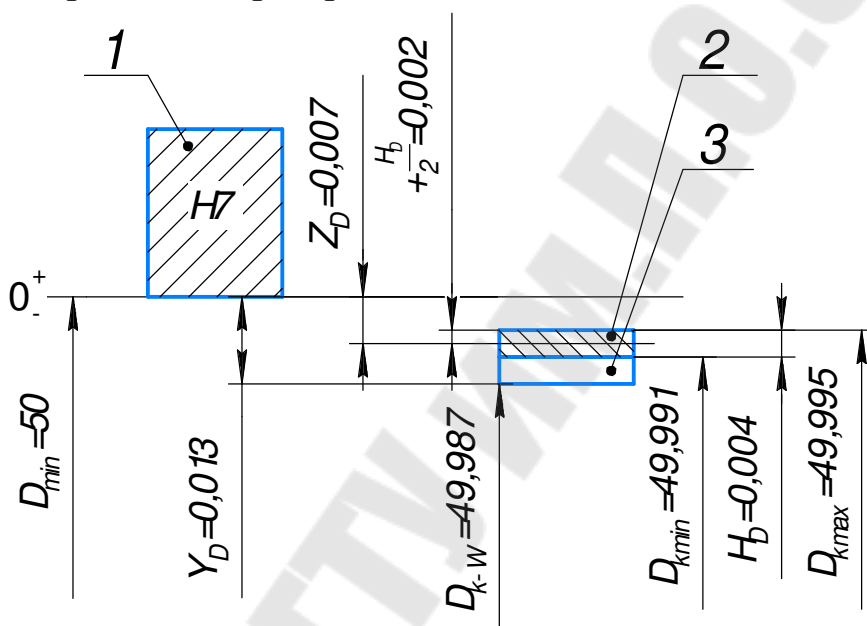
Схема расположения полей допусков диаметра D калибра пробки: 1 – поле допуска диаметра D втулки; 2 – поле допуска на изготовление калибра-пробки; 3 – поле износа калибра-пробки.
